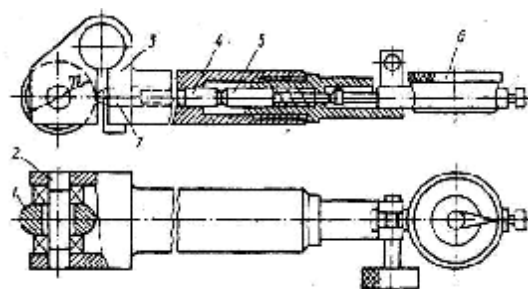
Пристрій для накатування канавок на зовнішніх циліндричних поверхнях: 1 – ролик; 2 – вісь; 3 – корпус; 4 – штовхач; 5 – стрижень; 6 – індикатор годинникового типу; 7 – упор
